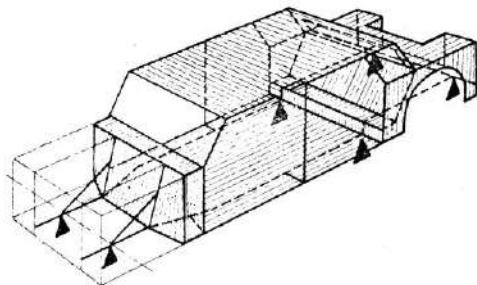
Схема корпусу кузова легкового автомобіля
